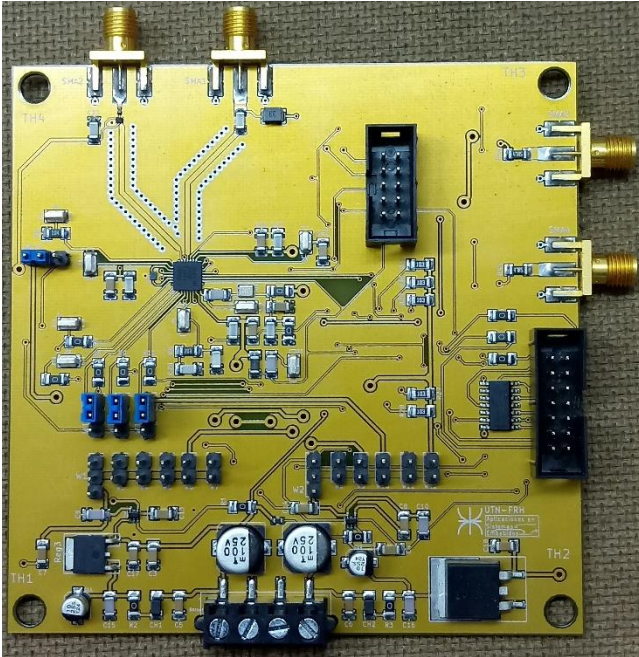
Cara superior de placa PCB del *front end* MAX2769.
